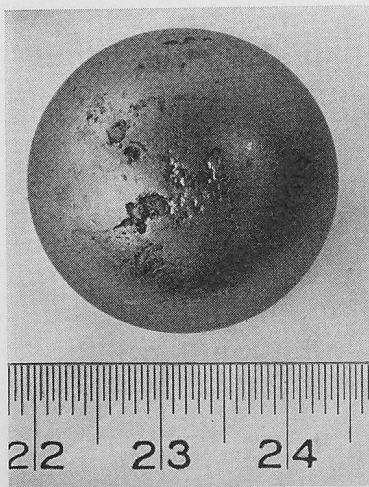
Kugel aus dem Lager einer Kranlaufrolle nach 12 Jahren Betrieb ohne Fetterneuerung. Oberfläche beschädigt, aber noch funktionsfähig
